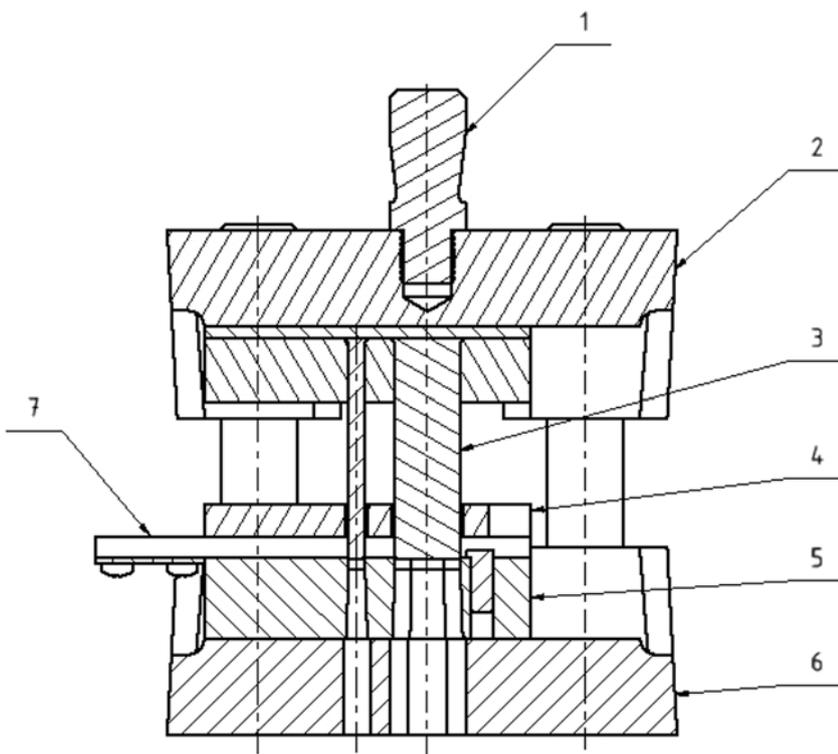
Folgeschneidwerkzeug für Platte mit zwei Bohrungen
